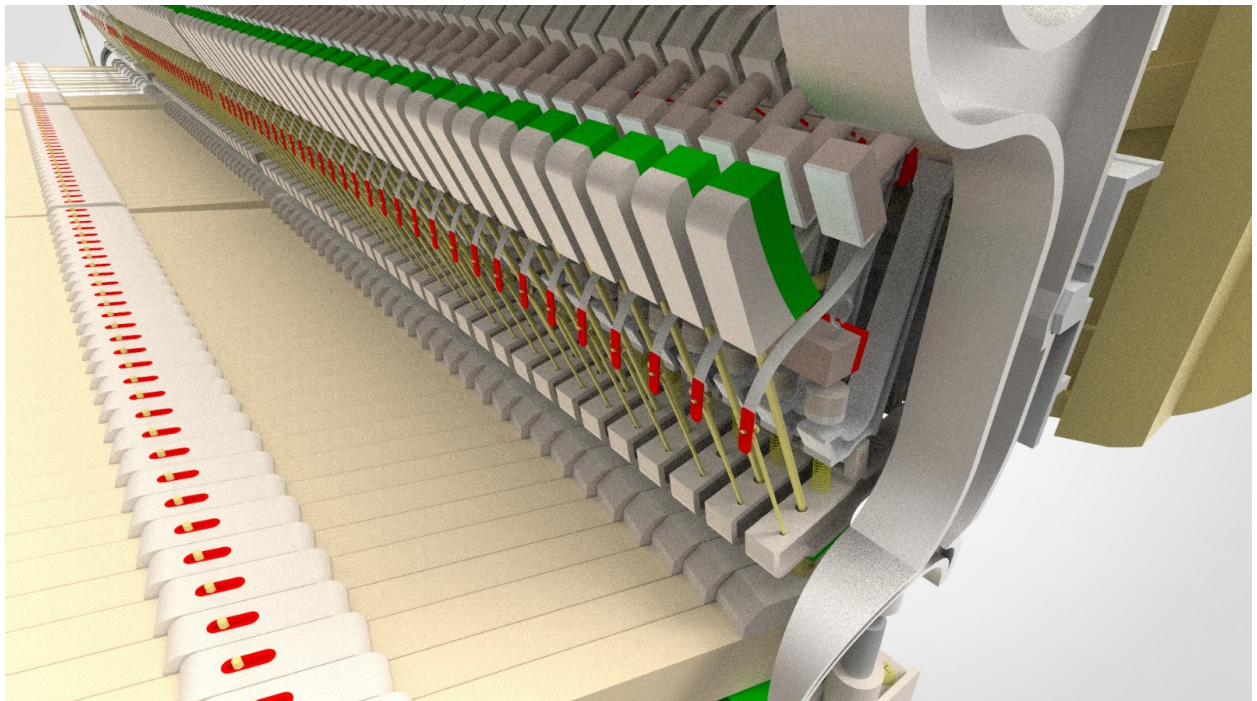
Detalle mecanismo (renderizado). Fuente: elaboración propia.
